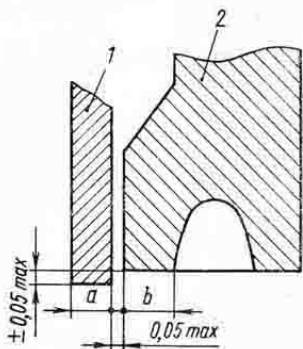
Конструкция соединения корпус (1) — основание (2), выполняемого лазерной сваркой; $a + b \leq \leq 1,5$ мм; $a/b = 0,5 \div 2$
